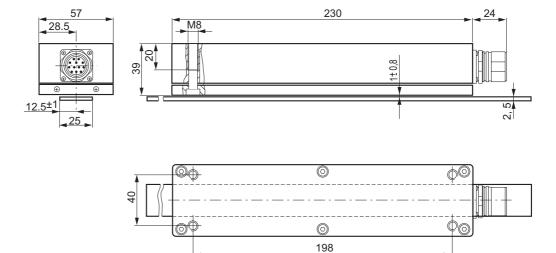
Desenhos das dimensões e tolerâncias de posição
